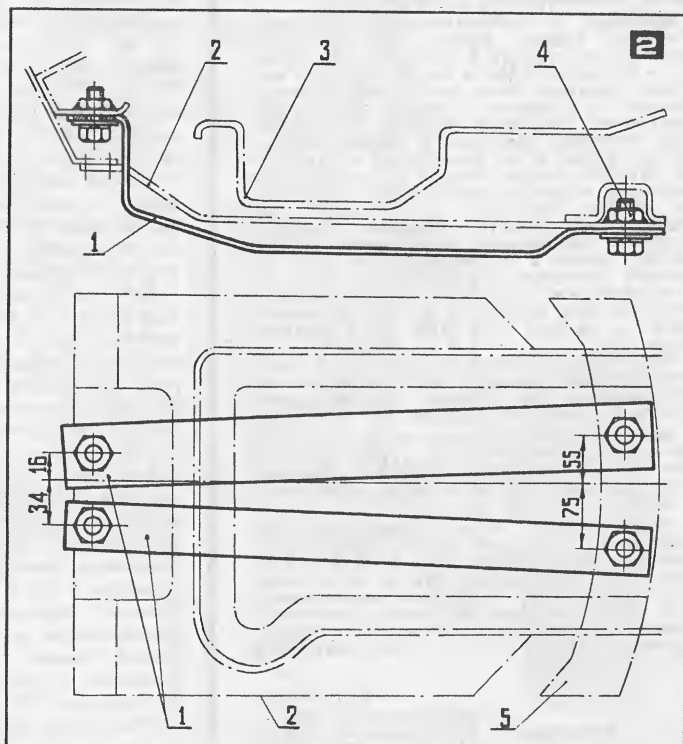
Установка защитных пластин: 1 — защитные пластины; 2 — брызговики; 3 — масляный поддон двигателя; 4 — болт М8×25 (4 шт.); 5 — поперечина передней подвески.
